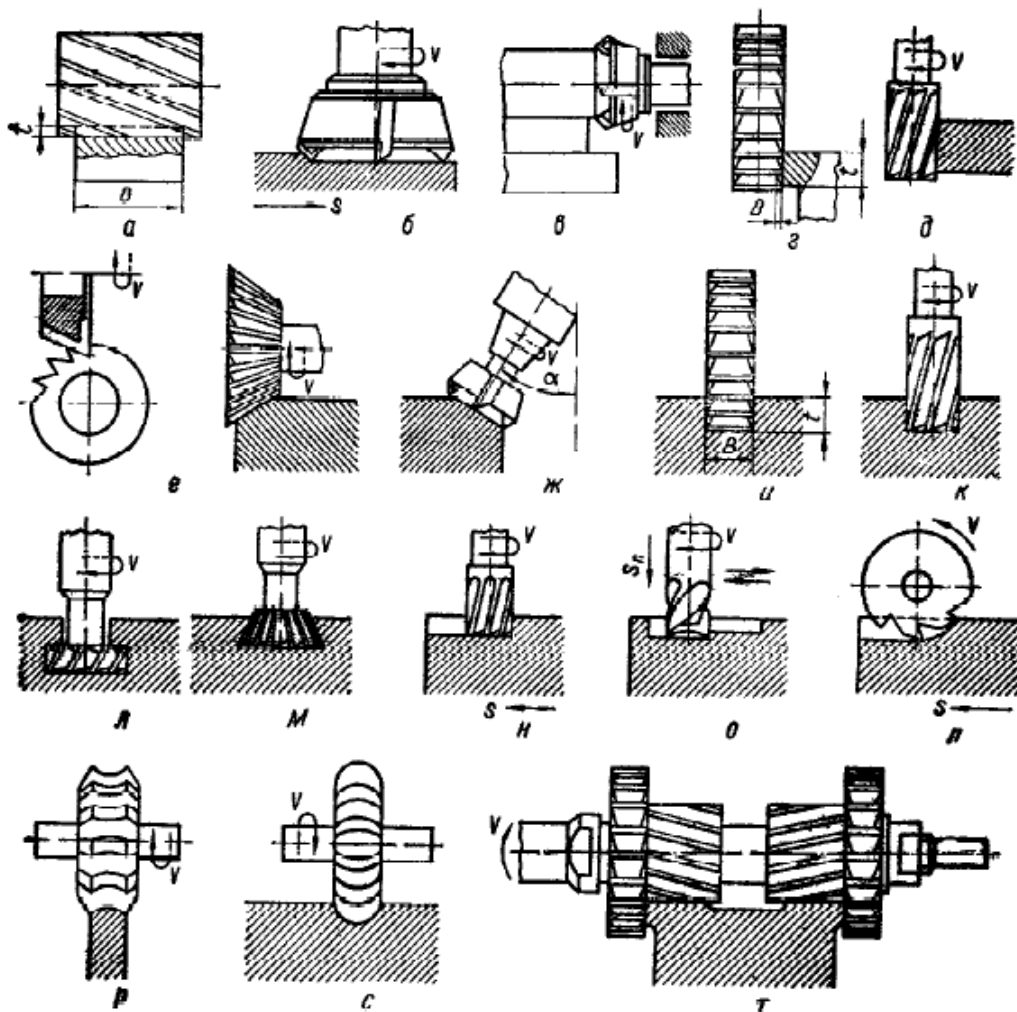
Приклади робіт, які виконують на фрезерних верстатах
